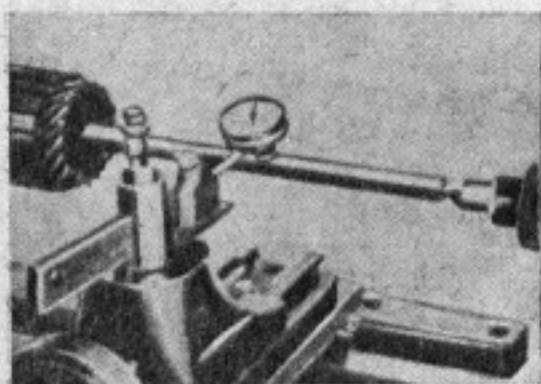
Проверка вала якоря стартера МАФ индикатором в токарном станке
